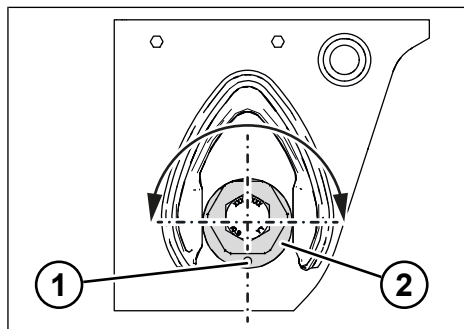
Upevnění šroubového spojení měchu pneumatického odpružení
